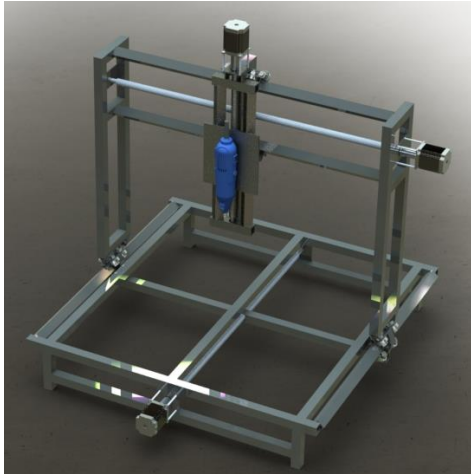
vista Isométrica del diseño de la fresadora CNC.
